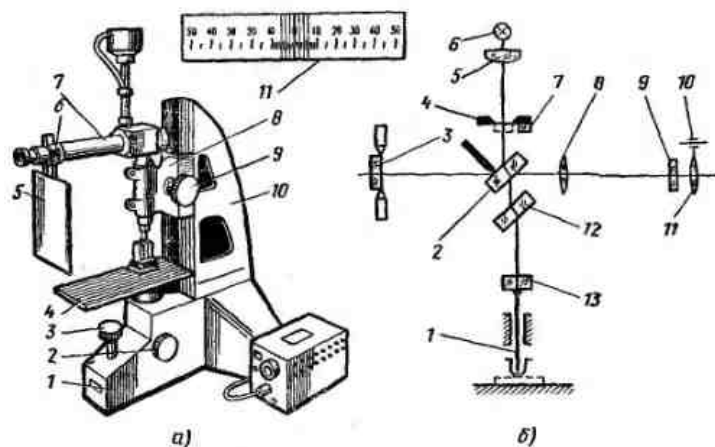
Вертикальный контактный интерферометр типа ИКПД
